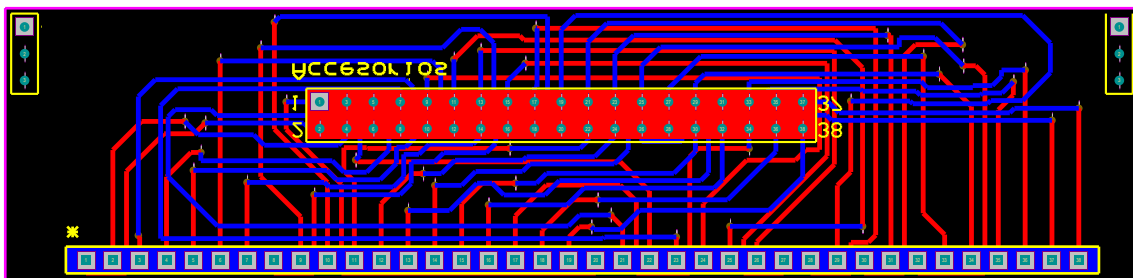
PCB conector Parte 2 del Módulo Principal.
